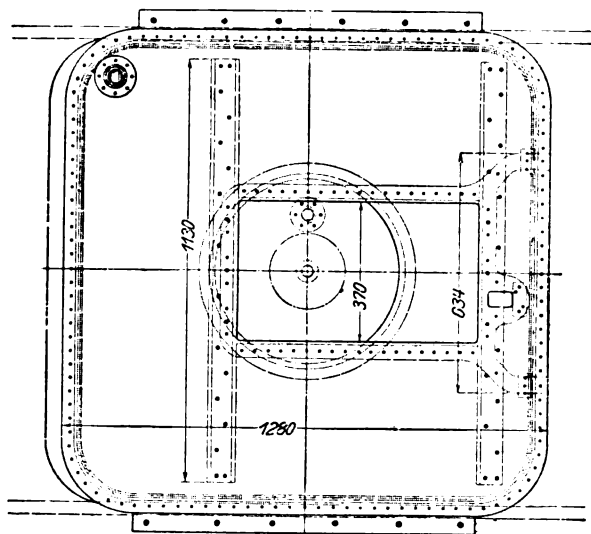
Vista degli anelli di contatto di un gruppo motore.
